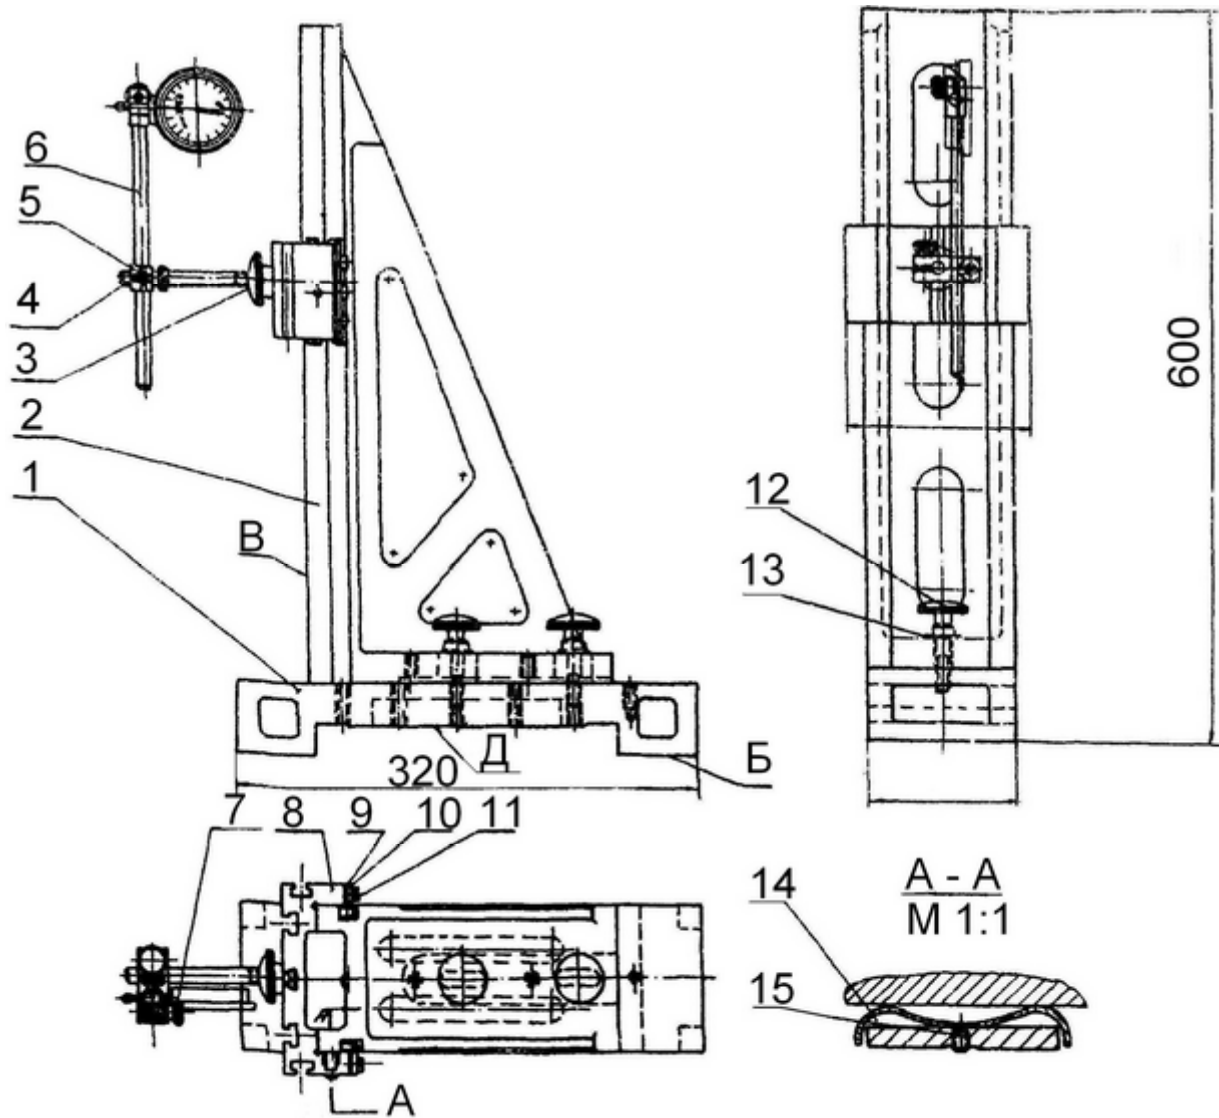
Приспособление для проверки перпендикулярности направляющих консоли к направляющим станины фрезерного станка СД 8532 – 4002
